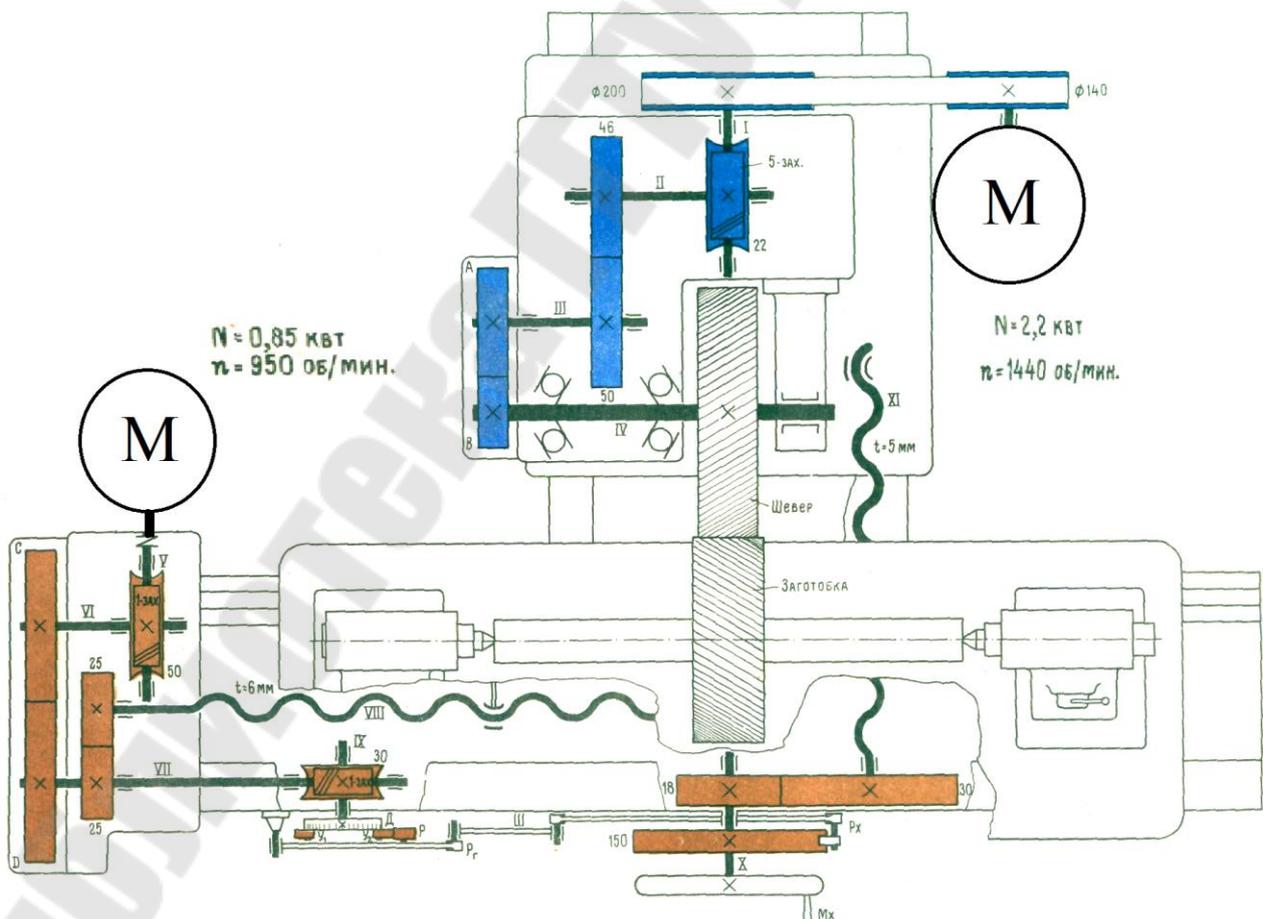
Кинематическая схема зубошевинговального станка
